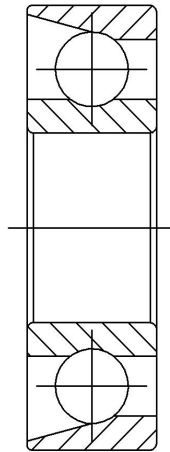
Кульковий підшипник радіально-упорний
